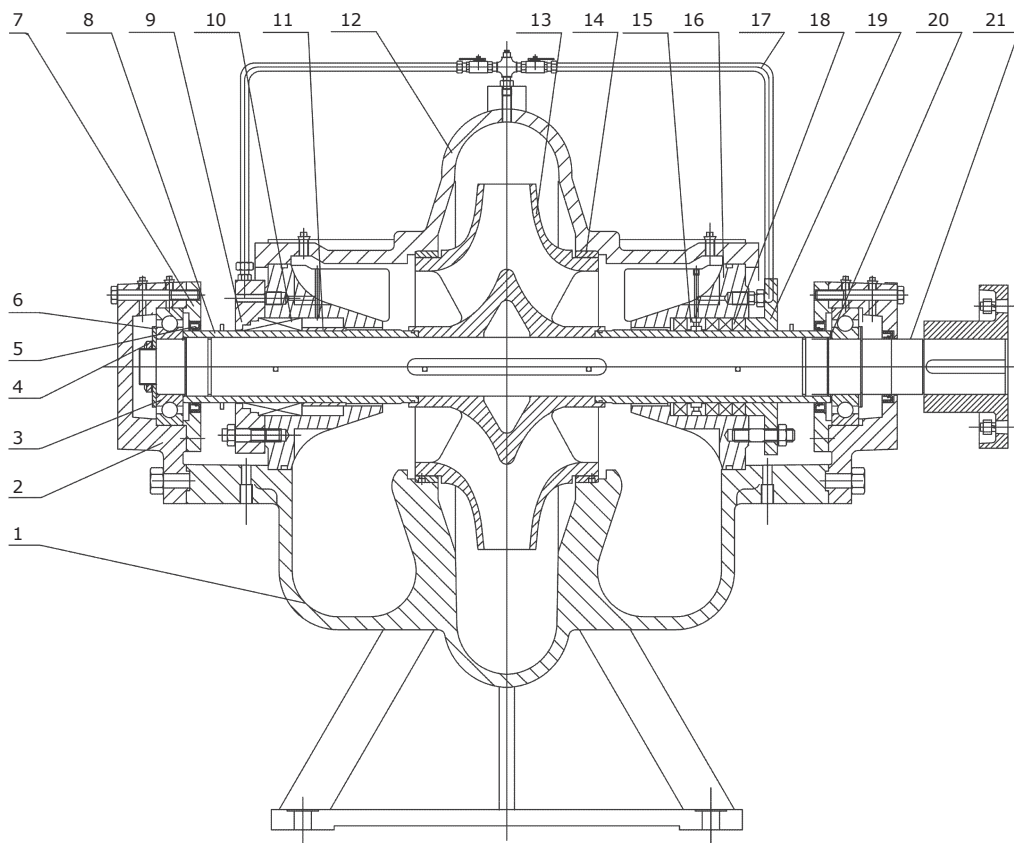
Вид в разрезе, стандартный тип исполнения 1
